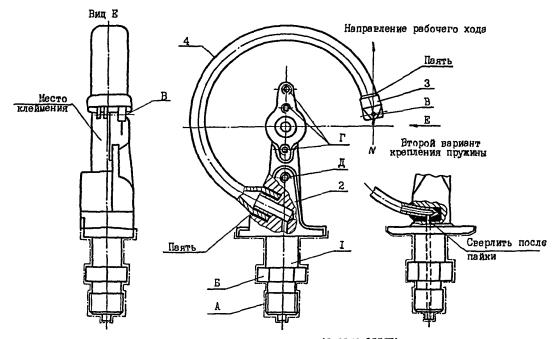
Держатель с пружиной (3.6816.011CE) Поз.2; 4 и ІЗ. Рис.2
